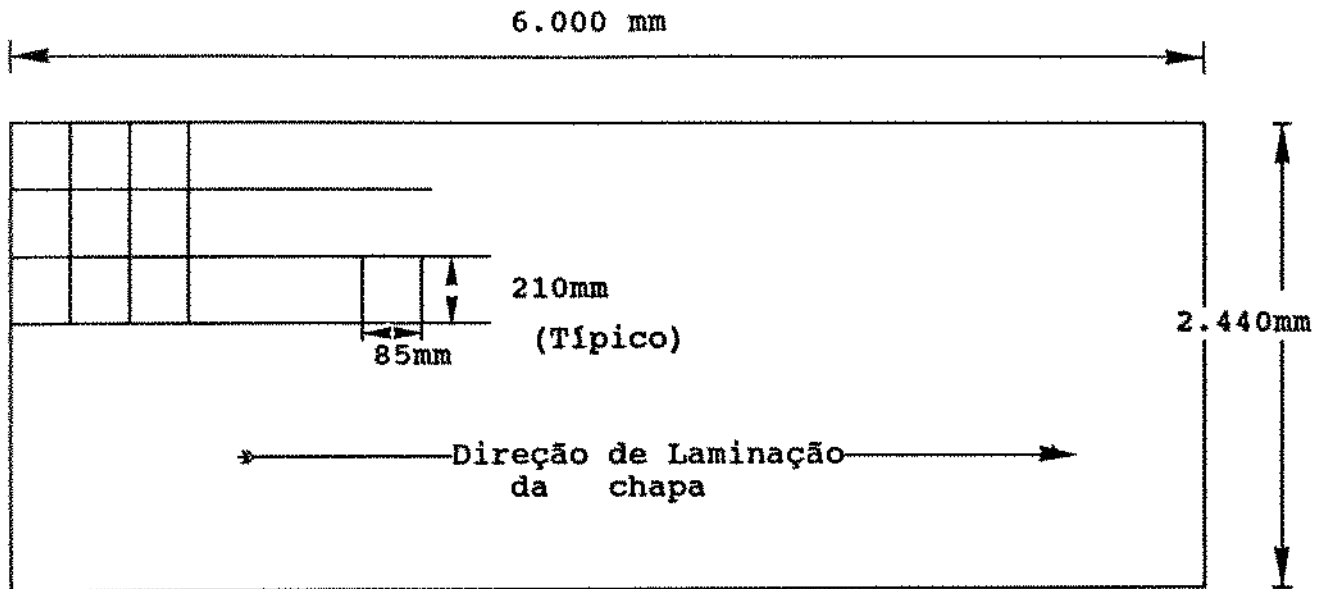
Esquema de retirada de chapas para corpos de prova
